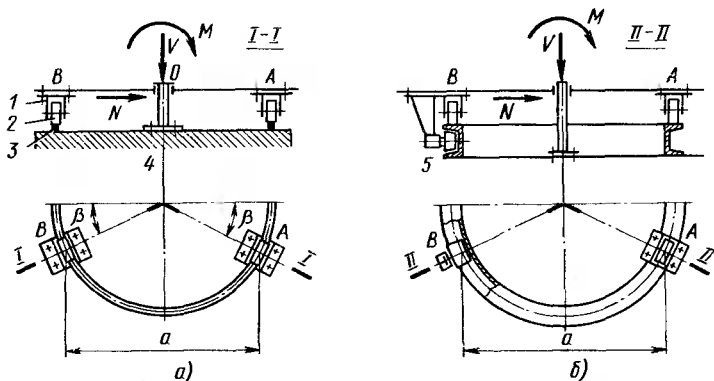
Схема малоопорного опорно-поворотного устройства:
